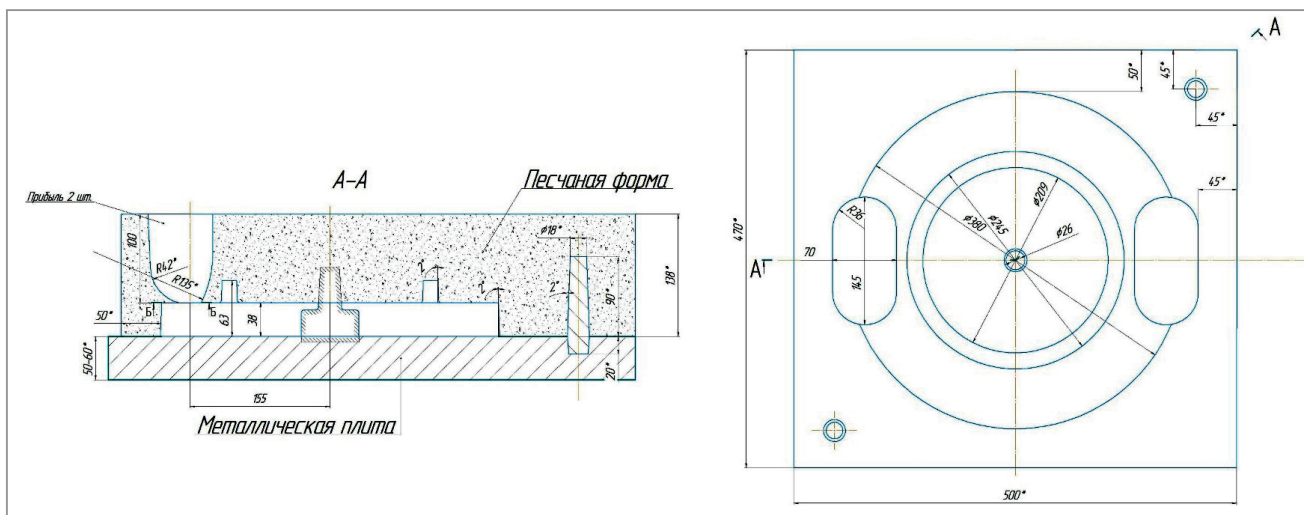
Литейная форма для изготовления отливок «Питающий диск» с использованием внешнего металлического холодильника
